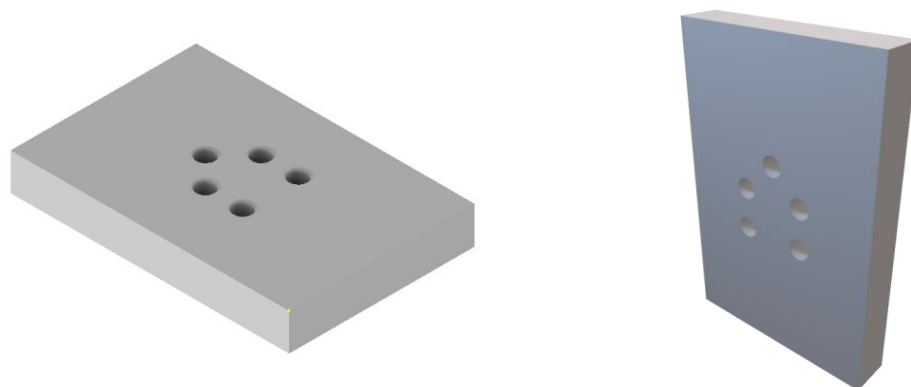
Τρισδιάστατη απεικόνιση αποστολής 44
